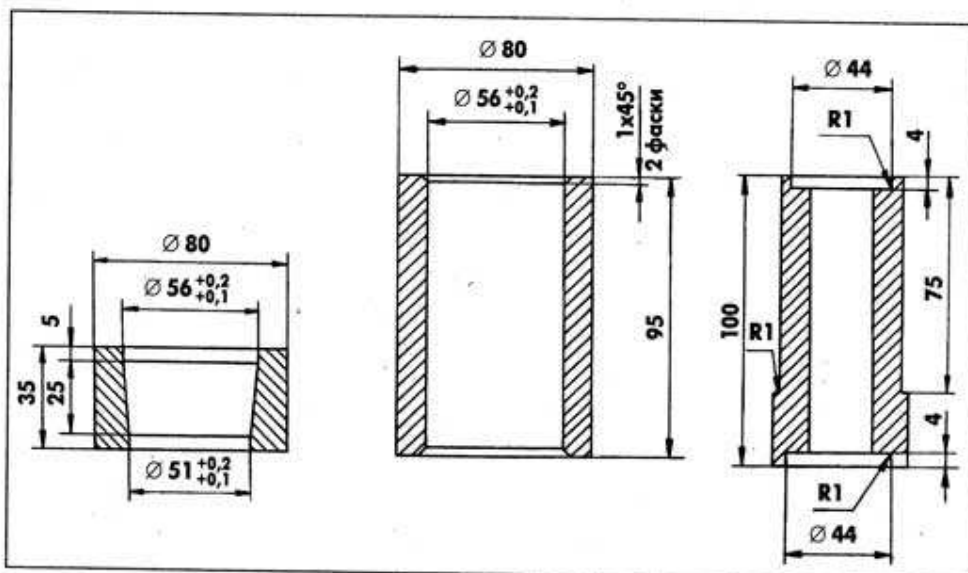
Оправки для запрессовки резинометаллических шарниров в ушко рессоры и кронштейны. Материал – сталь 40X (HRC 30–34)
